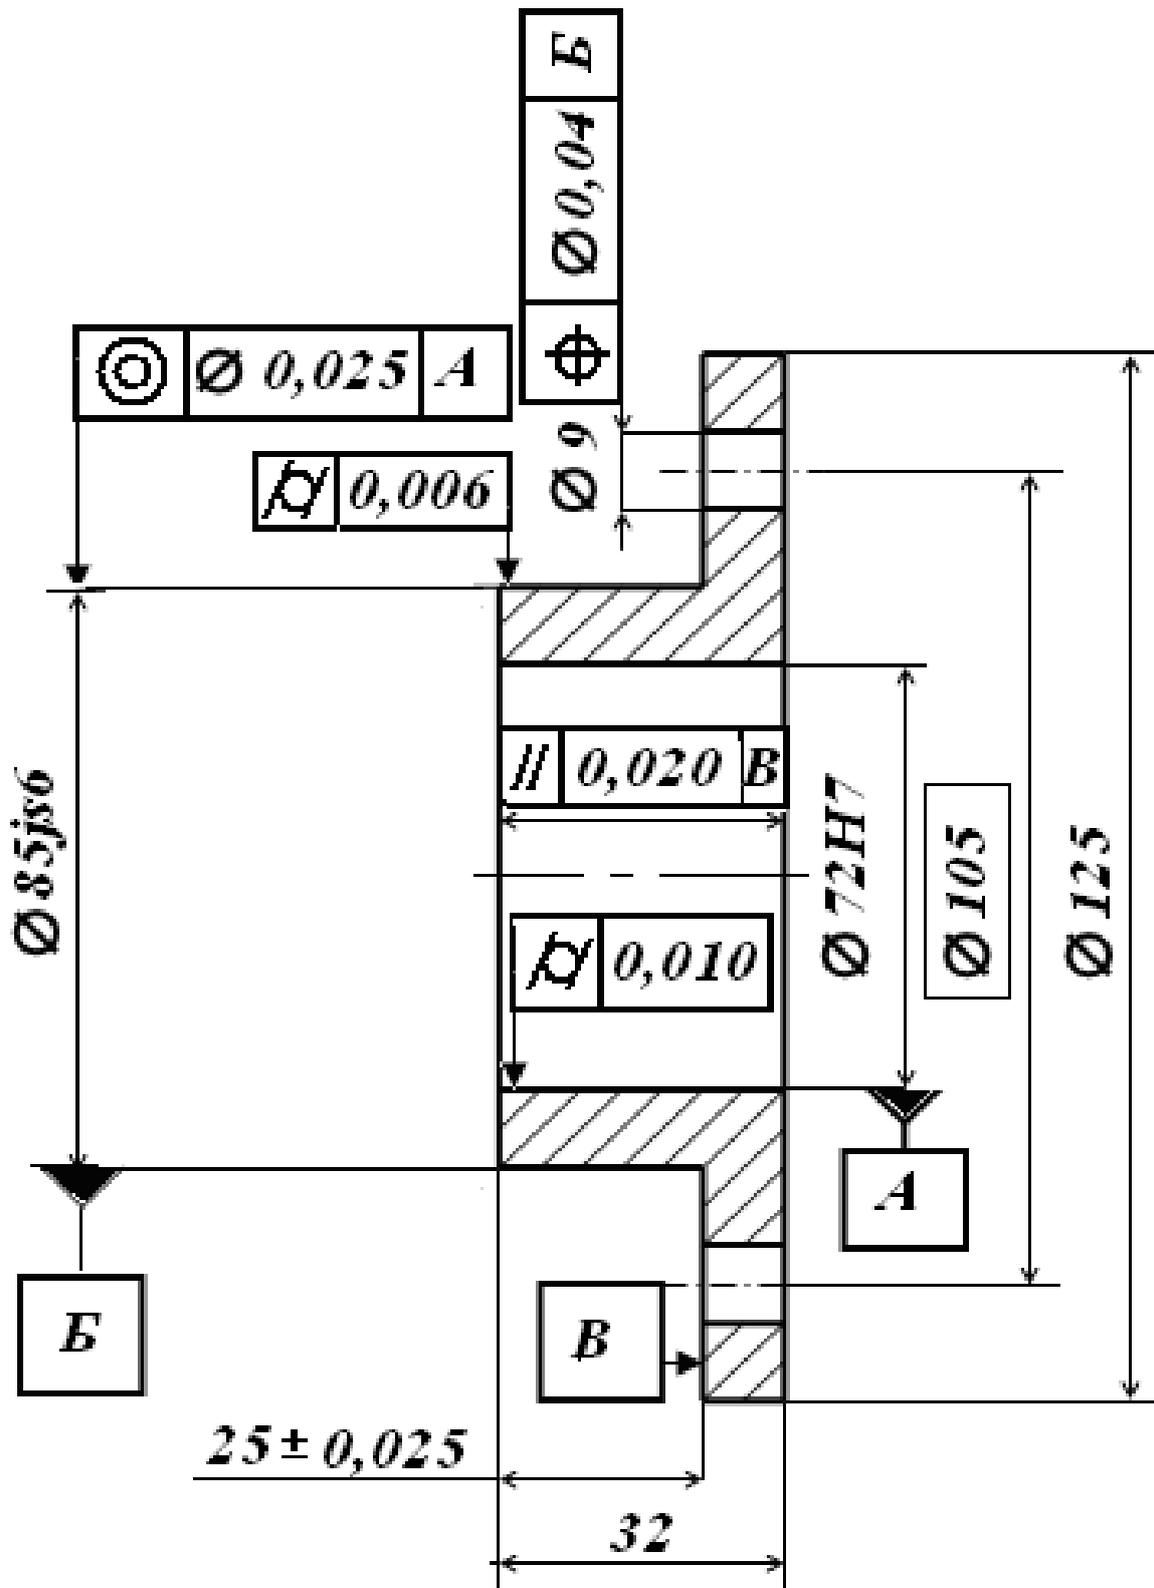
Ескіз стакана з зазначенням баз і допусків форми і розташування поверхонь
